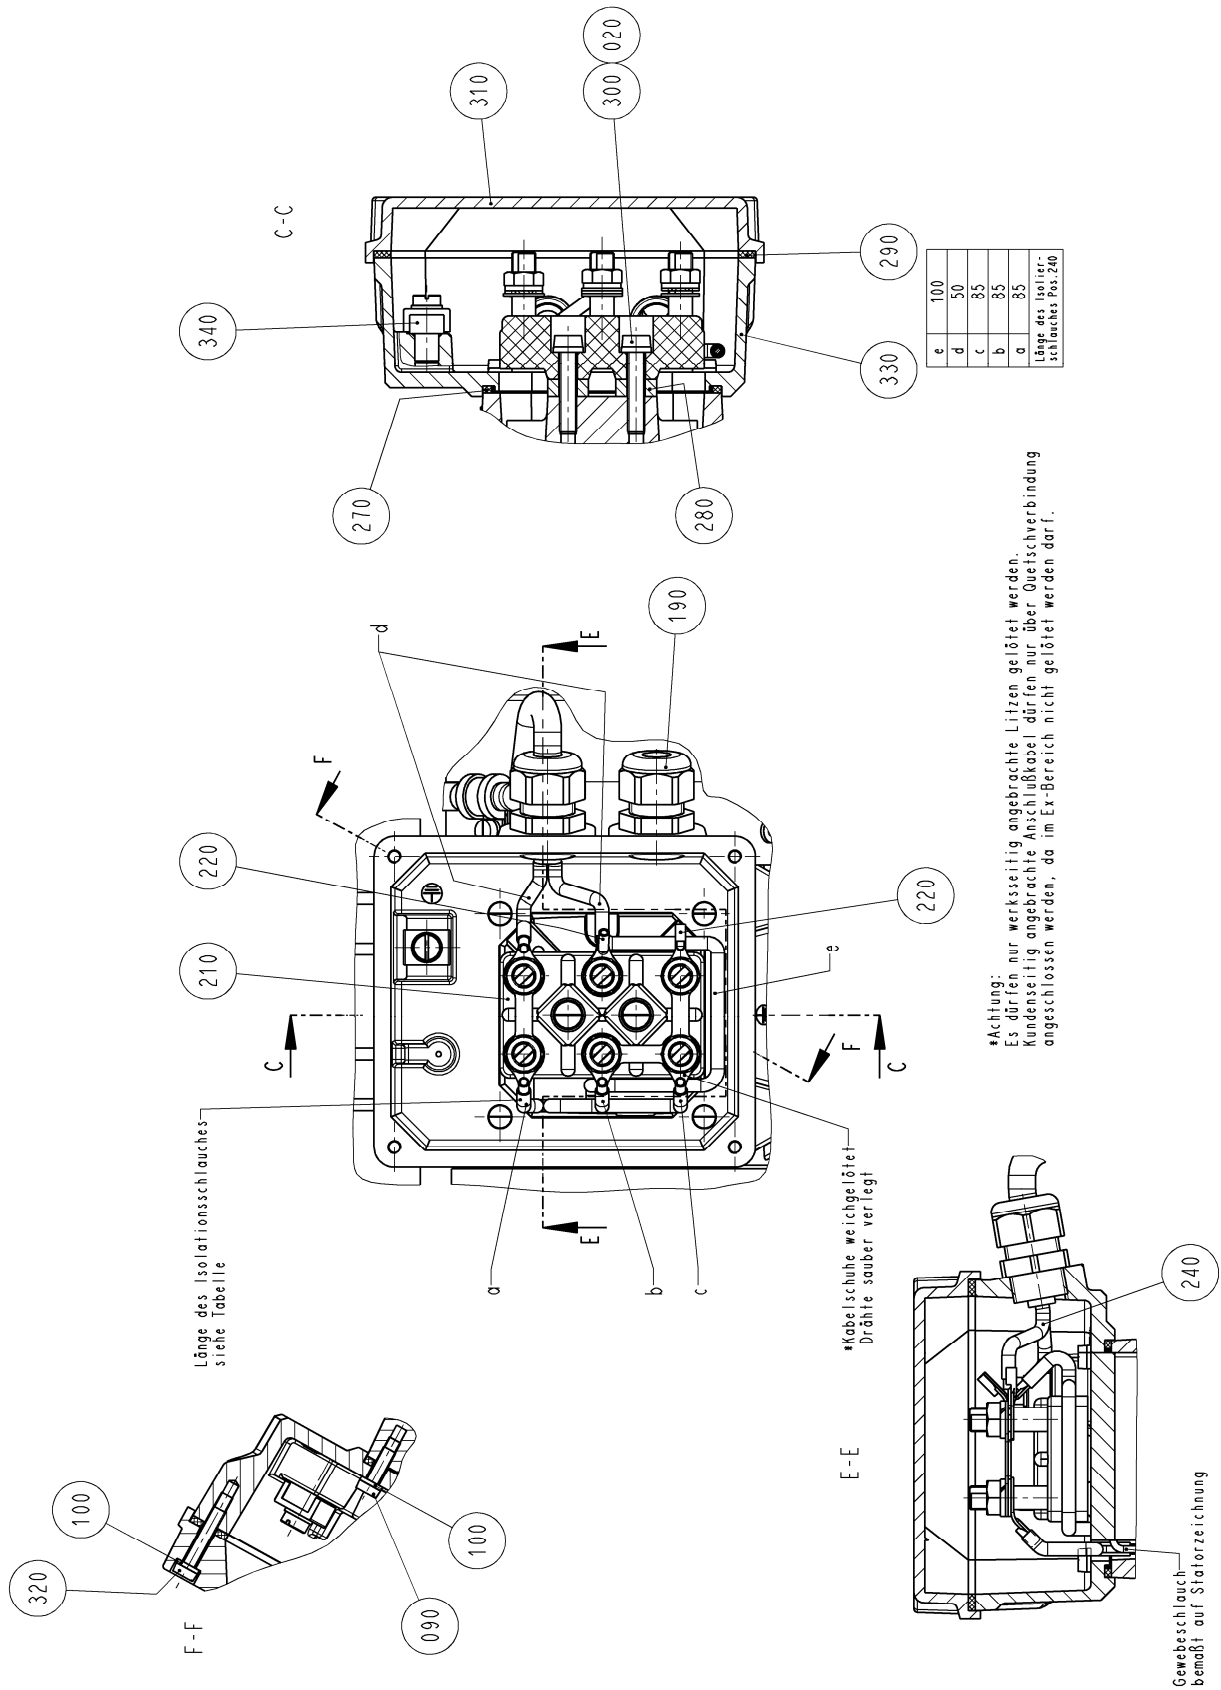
Klemmkasten Explosionsgeschützter Kondensatormotor
